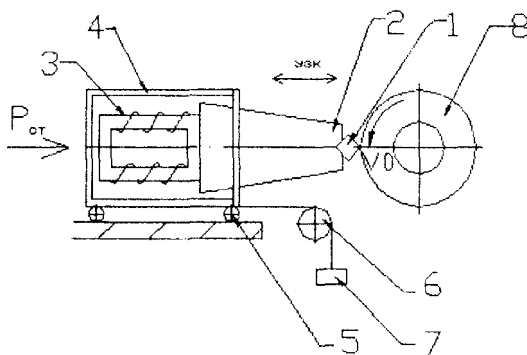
Схема механического распиливания при сообщении заготовке ультразвуковых колебаний
